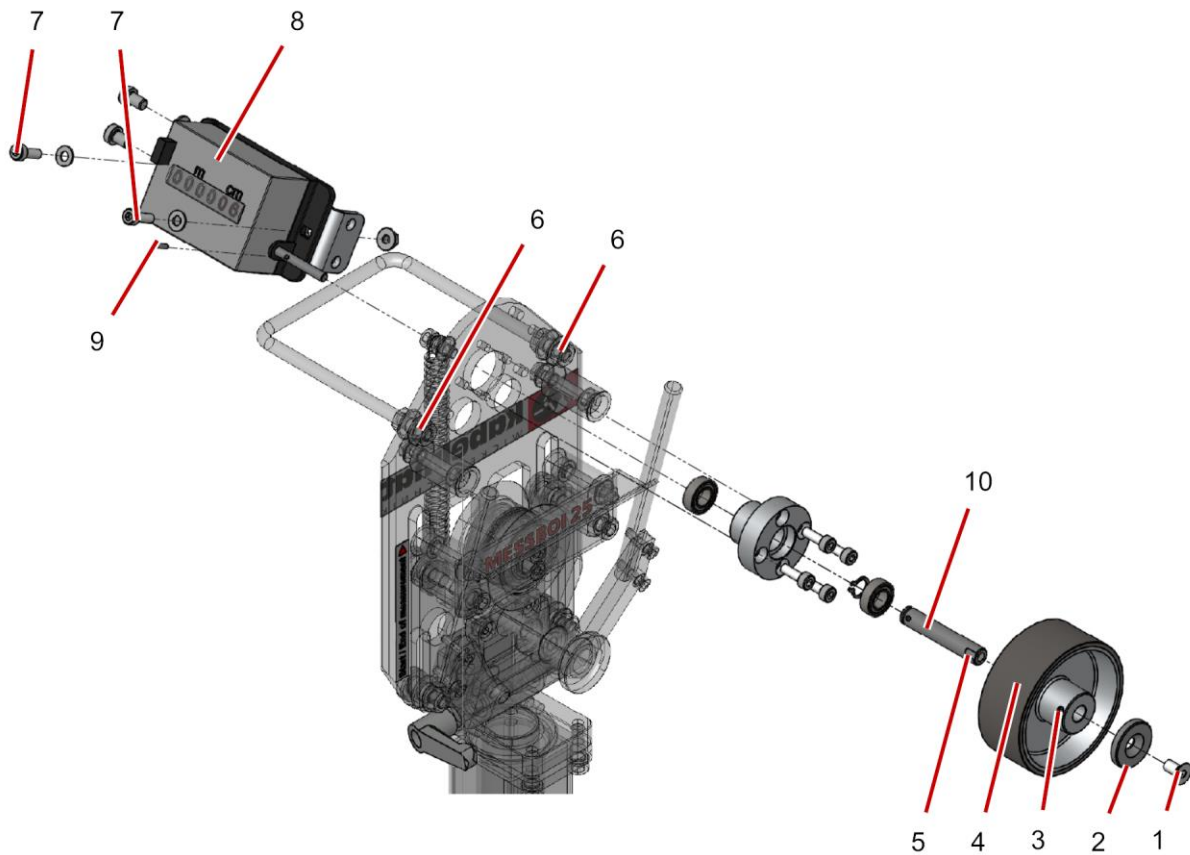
Remplacer le compteur / la roue de mesure - MESSBOI 25
